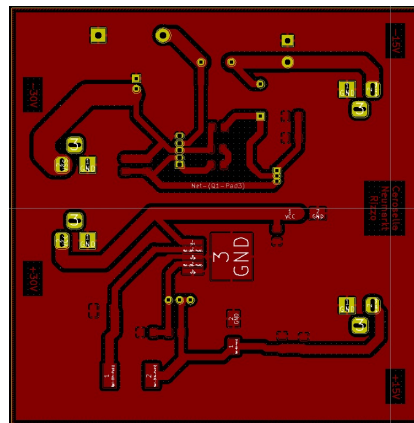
Vista de las pistas del PCB de la fuente a implementar
